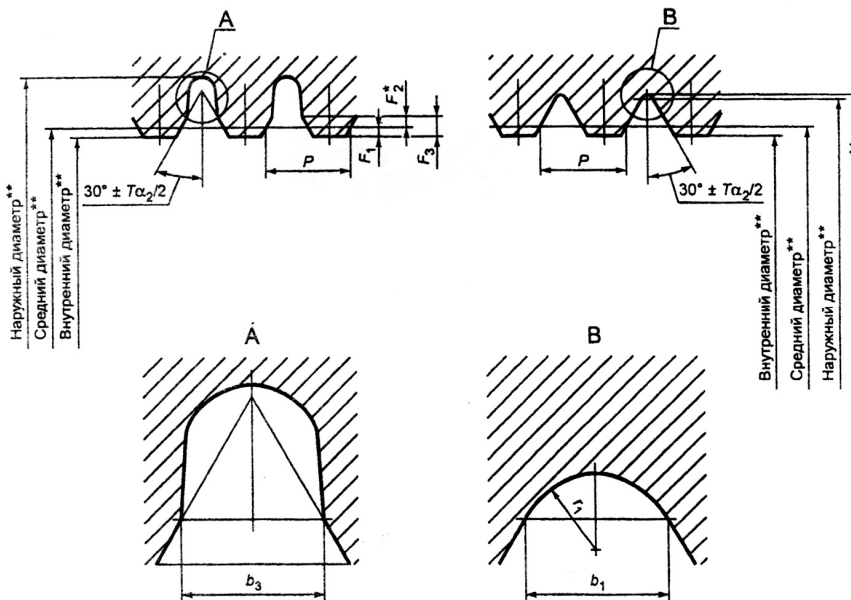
Полный профиль резьбы $M36 \times 1-7g6g-14$ калибров-колец видов ПР(1), ПР(4) и калибра-скобы вида ПР(7), выполненный с канавками или с радиусами, мм
